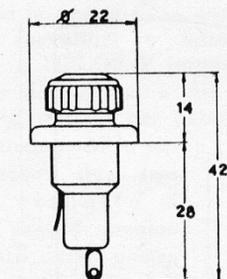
Dimensioni del fusibile 1039 e piano di foratura sul telaio.
